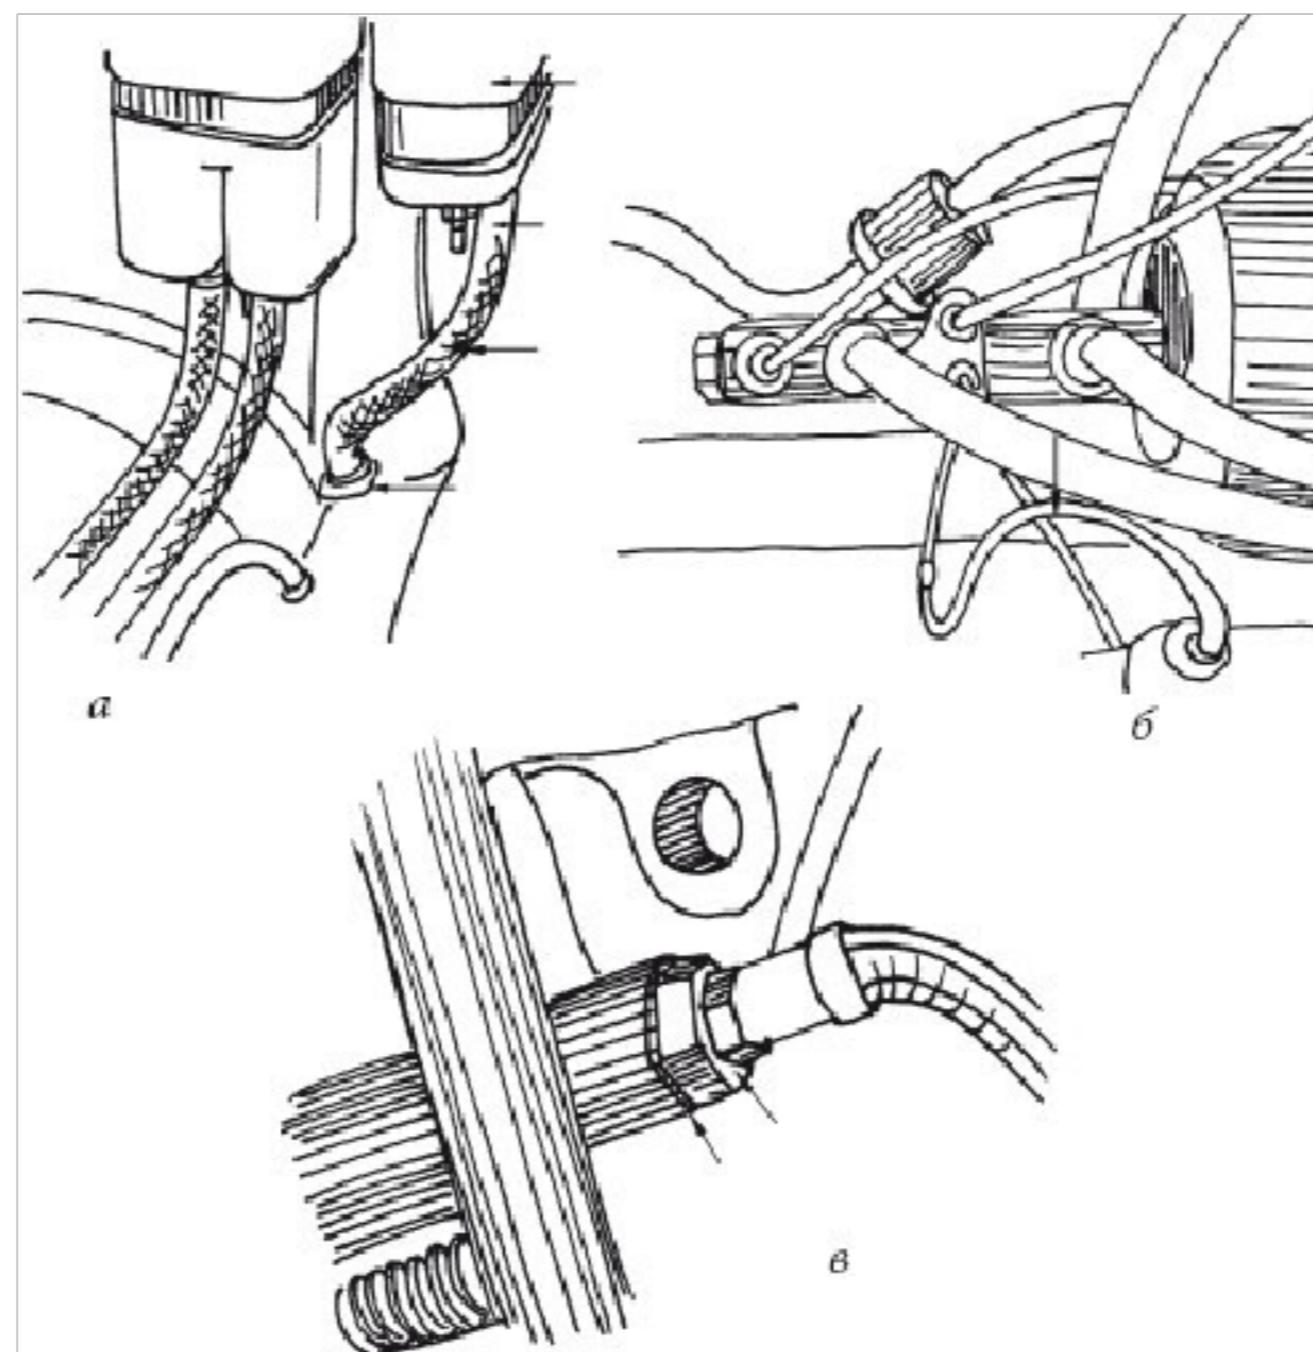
Основные узлы системы сцепления, требующие проверки: а – бачок и штуцер основного цилиндра, б – главный цилиндр, в – место соединения шланга с рабочим цилиндром
